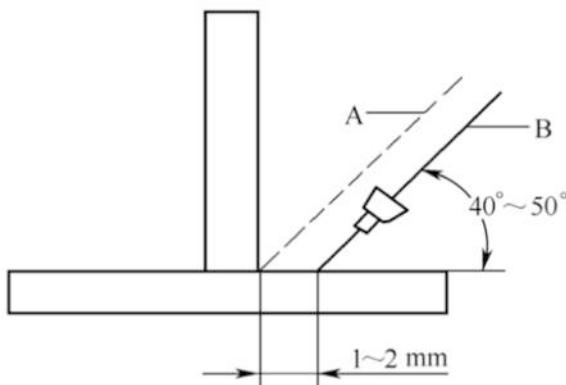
Угол наклона горелки при сварки Т-образных швов
